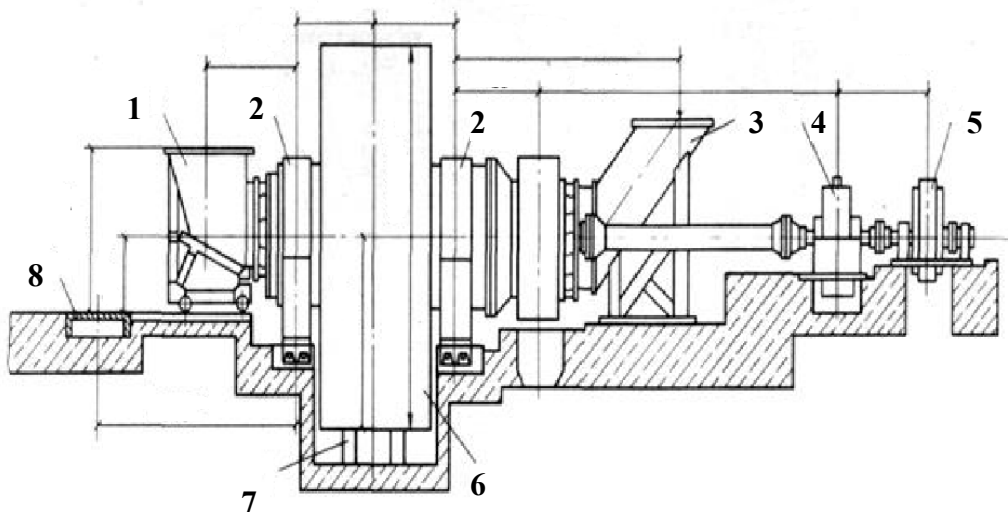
Кульовий млин: 1 – завантажувальна частина; 2 – підшипники; 3 – розвантажувальна частина; 4 – редуктор; 5 – електродвигун; 6 – барабан млина; 7 – пристосування для підймання барабана млина; 8 – пристосування для підймання завантажувальної частини
